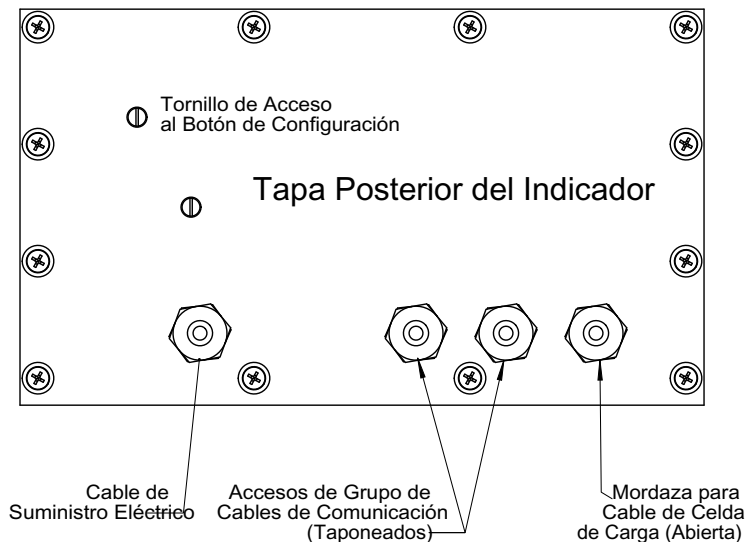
Asignaciones Recomendadas para las Mordazas de los Cables
